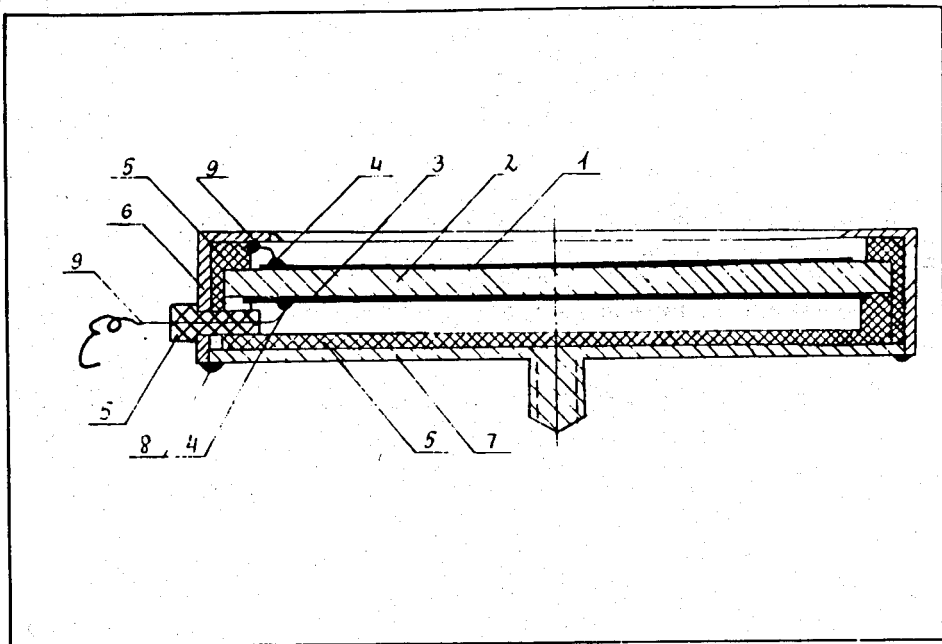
Упаковка детекторов, работающих при охлаждении. 1 - золотой электрод, 2 - пластина кремния, 3 - никелевый электрод, 4 - пайка выводов, 5 - тефлоновый изолятор, 6 - латунный корпус, 7 - латунная крышка с винтом, 8 - пайка крышки с корпусом, 9 - электрические выводы.
